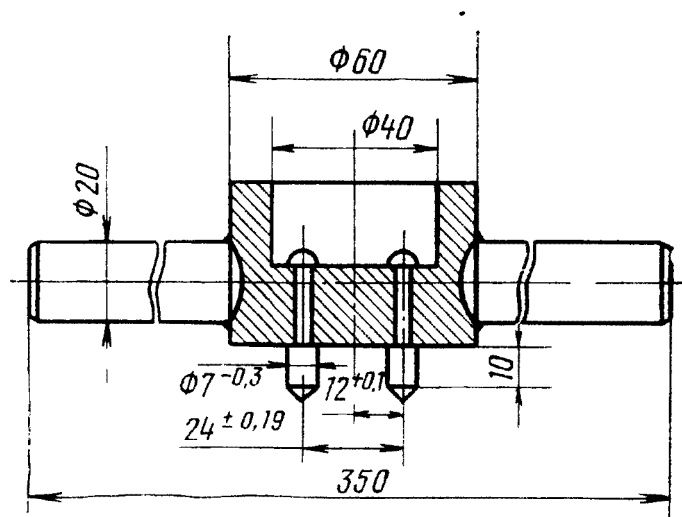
Ключ специальный для гайки шарнира гидроцилиндра рулевого управления
